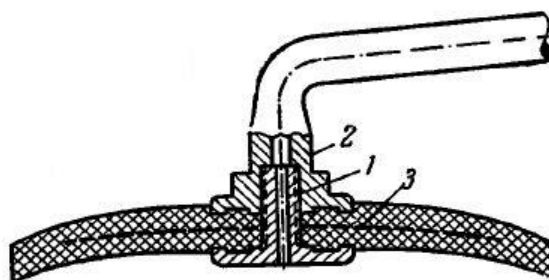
Вентиль металлический с резиновой пяткой, привулканизованной сверху камеры
